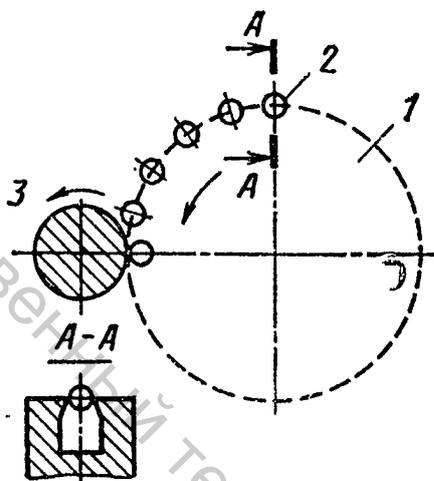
Схема центробежно-шариковой упрочняюще-чистой обработки: 1 – диск; 2 – шарики; 3 – обрабатываемая деталь
